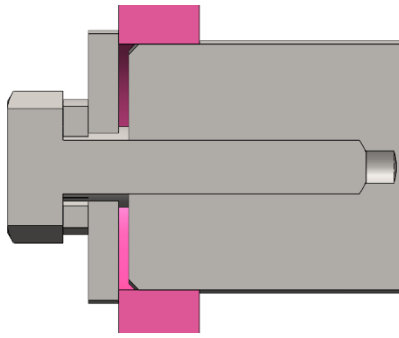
Vista detalle el encaje del eje de las poleas fijas (Fuente 34)
